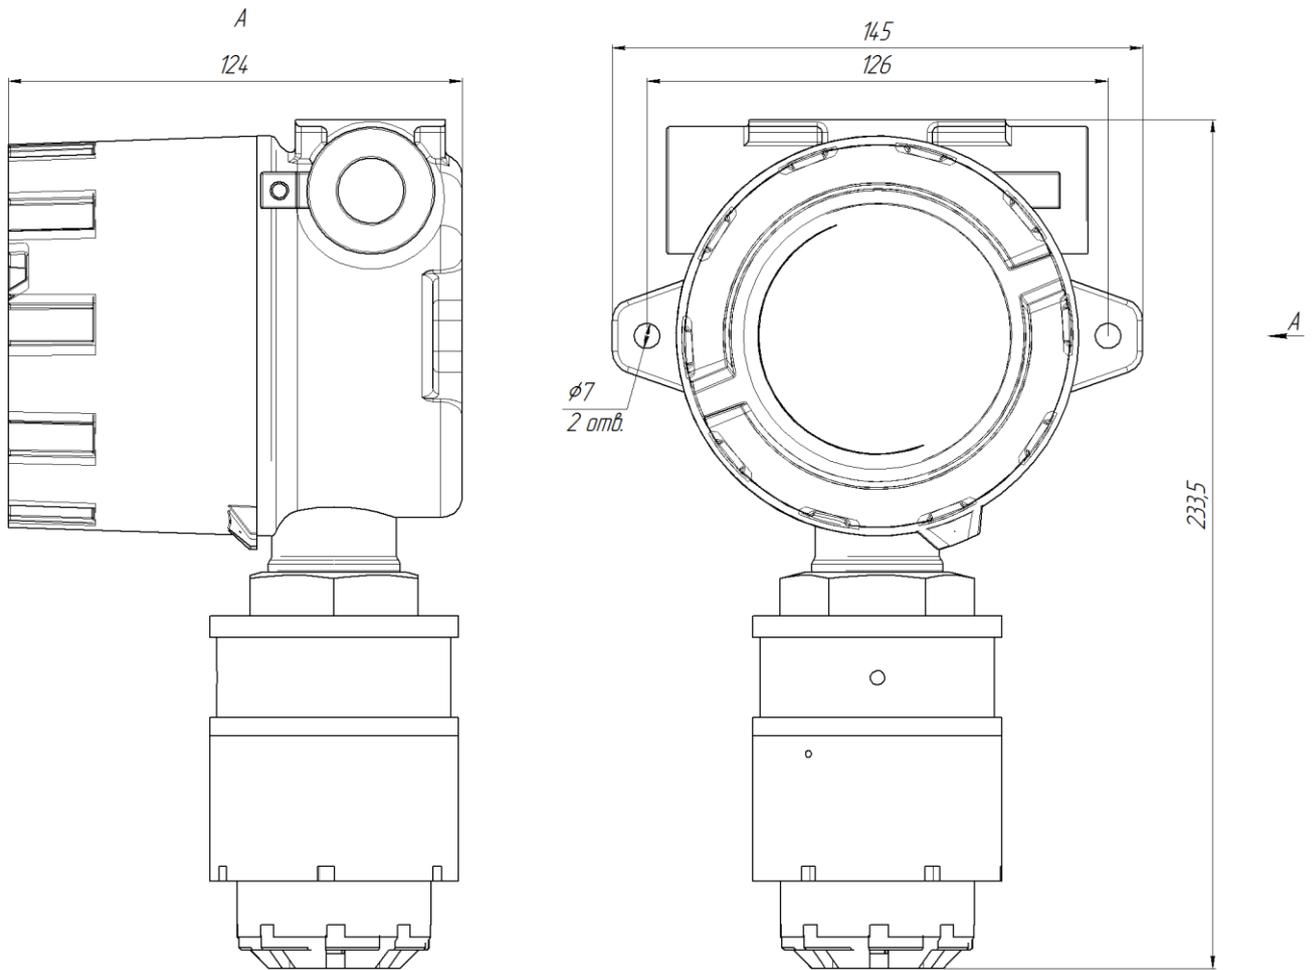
Габаритный чертеж ДГС ЭРИС-230.
